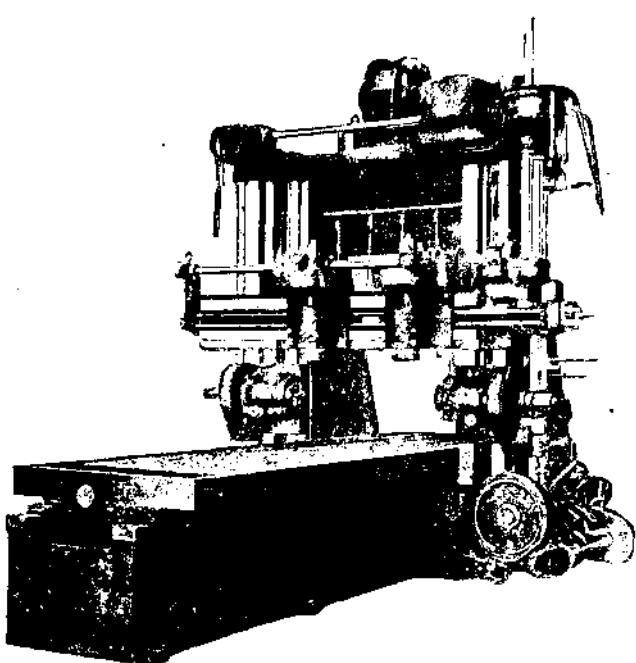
Стандартный продольно-фрезерный станок Ингерсоль.
